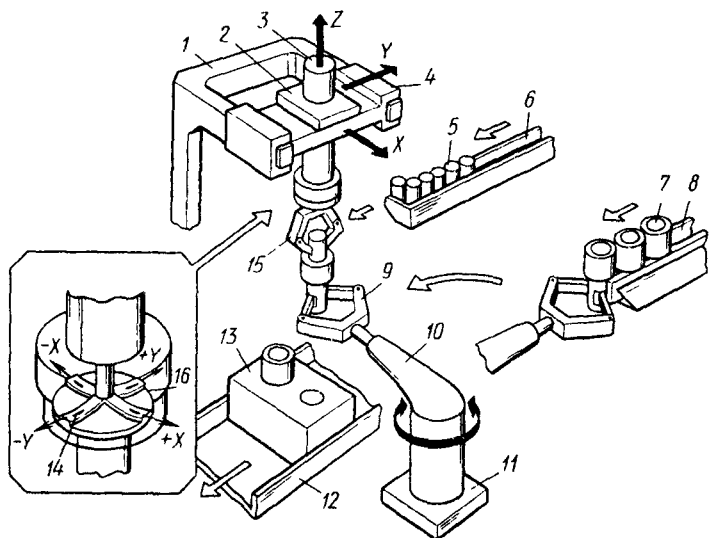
Схема сборки цилиндрических соединений с зазором на стенде
